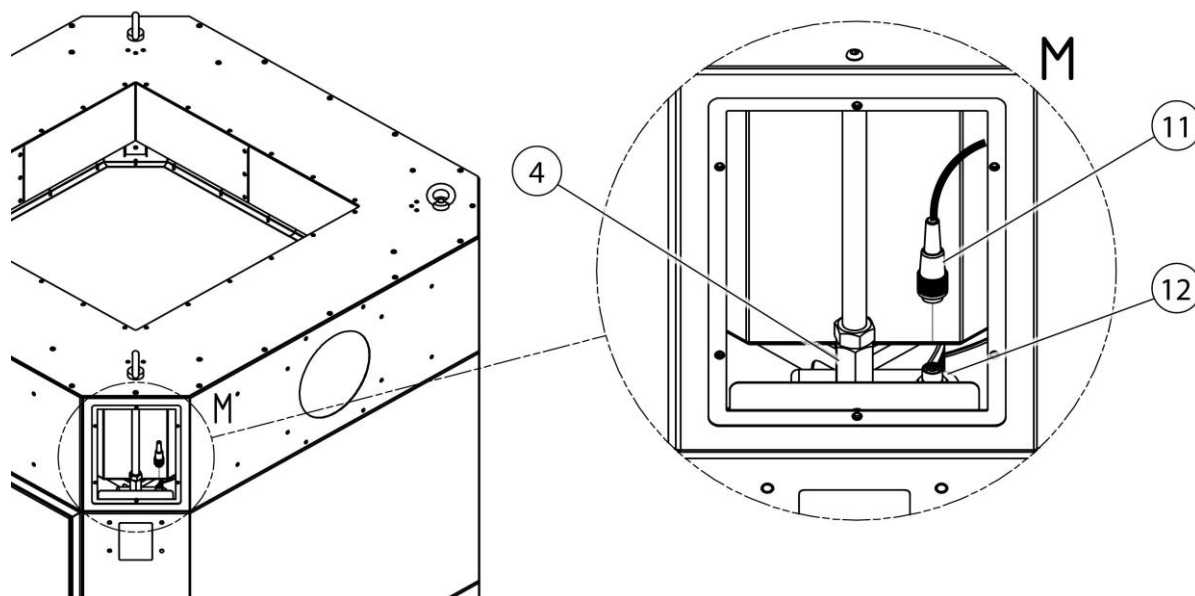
Montaggio - Gruppo aspirazione con gruppo filtro
